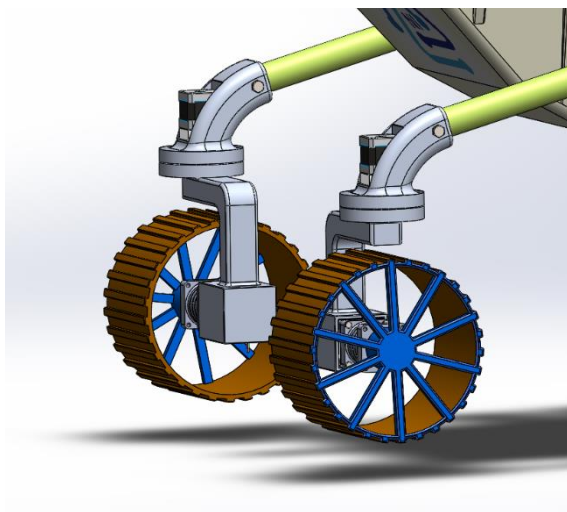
Загальна конструкція передньої рухомої частини підвіски
